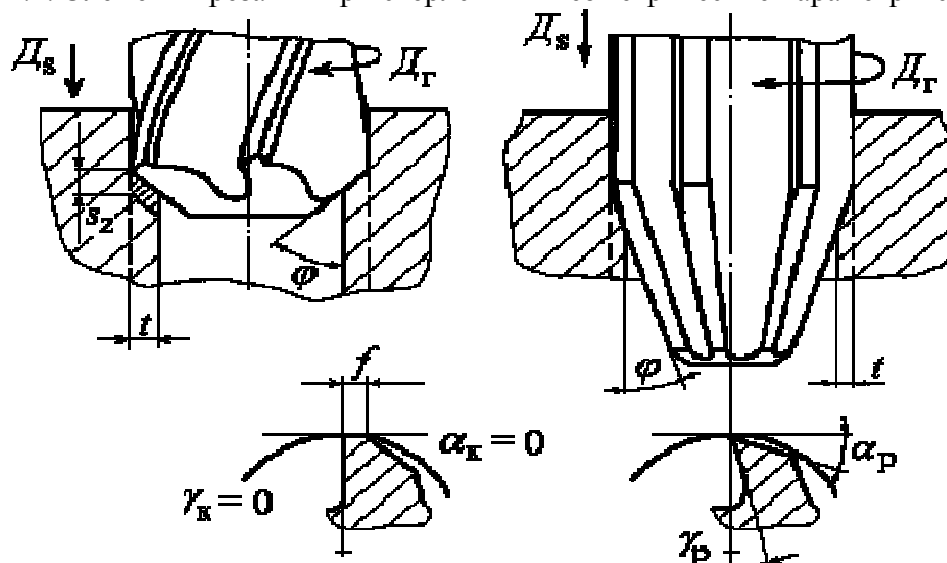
Элементы резания: а) - при зенкеровании, б) - развертывании; в) - профиль режущей и г) - калибрующей частей зуба развертки.
